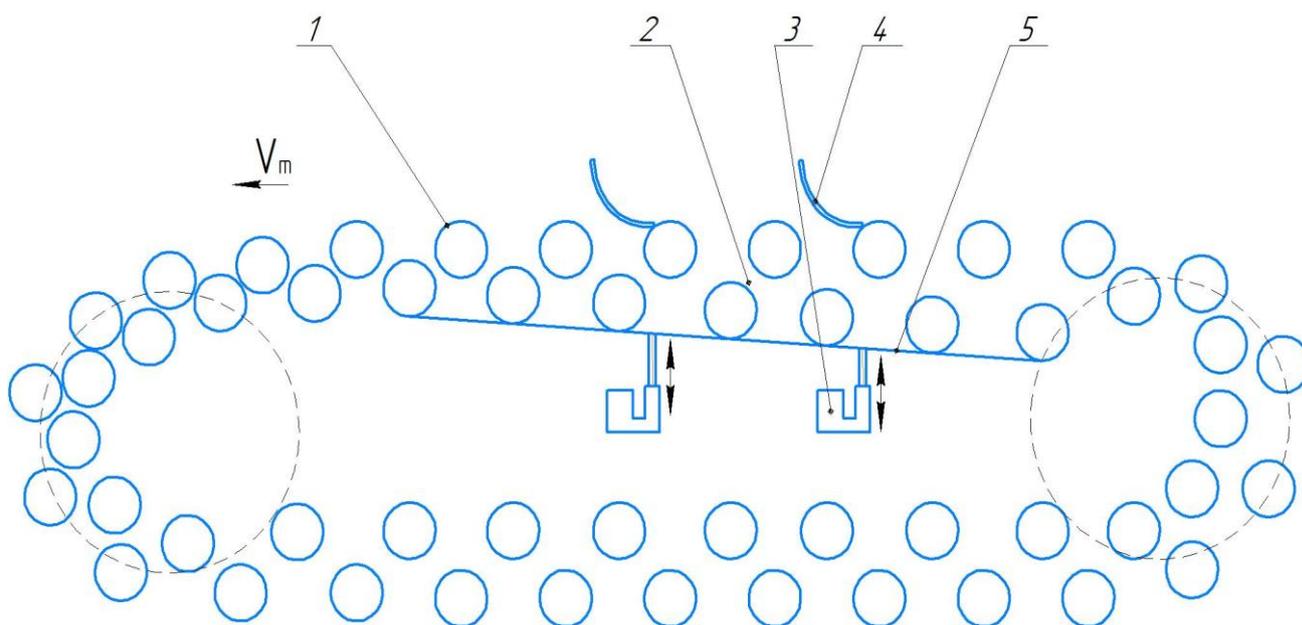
Принципиальная схема роликового калибратора с эластичными интенсификаторами: 1 - калибрующий ролик; 2 – калибрующие отверстия; 3 – регулировочное устройство; 4 – эластичный интенсификатор; 5 – направляющие опоры
